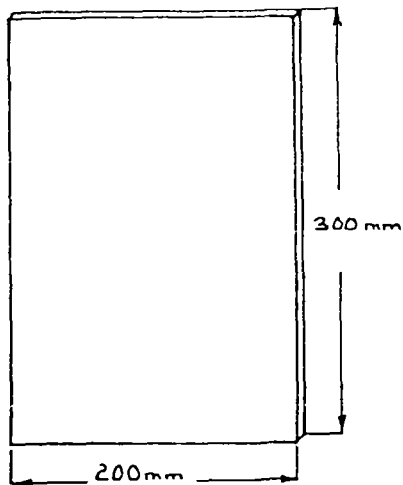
Dans un morceau de carton découper un rectangle de 300mmx200mm. Coller sur une face du papier blanc. En utilisant le compas tracer un cercle sur cette feuille.
